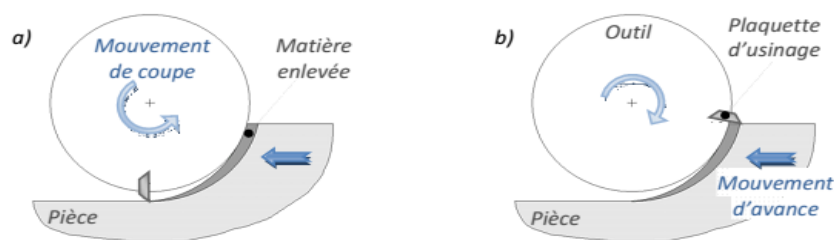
Configurations d'usinage en fraisage de profil[22].
